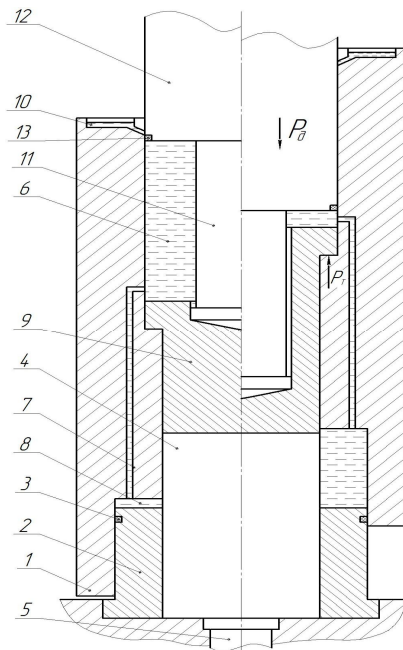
Схема ХВ з розтягненням стінки заготовки.
